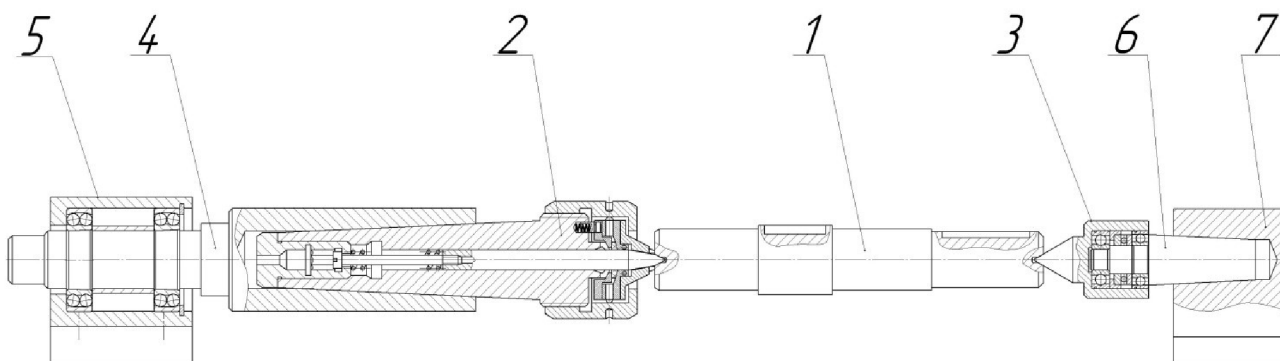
Механізм обертання вала черв'ячного редуктора
